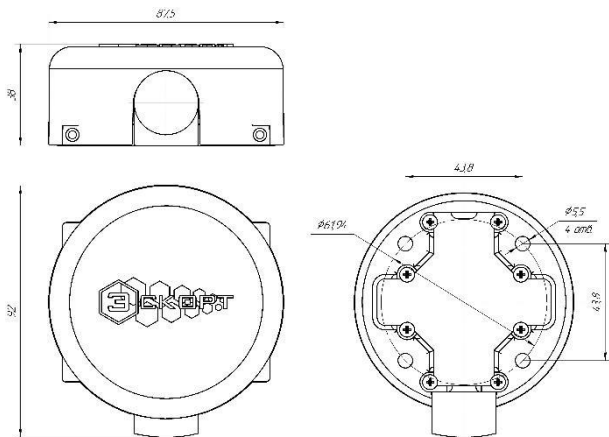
Габаритные и присоединительные размеры ESCORT TAG
